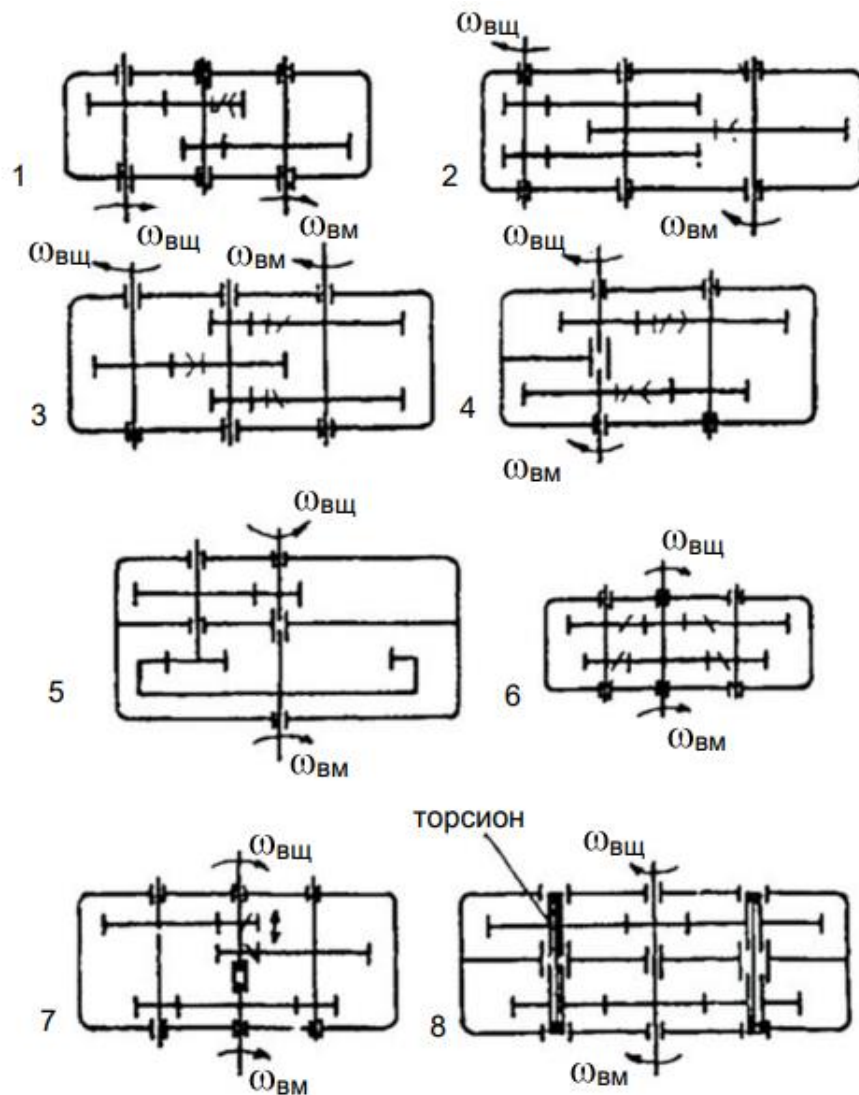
Схемы двухступенчатых цилиндрических редукторов
